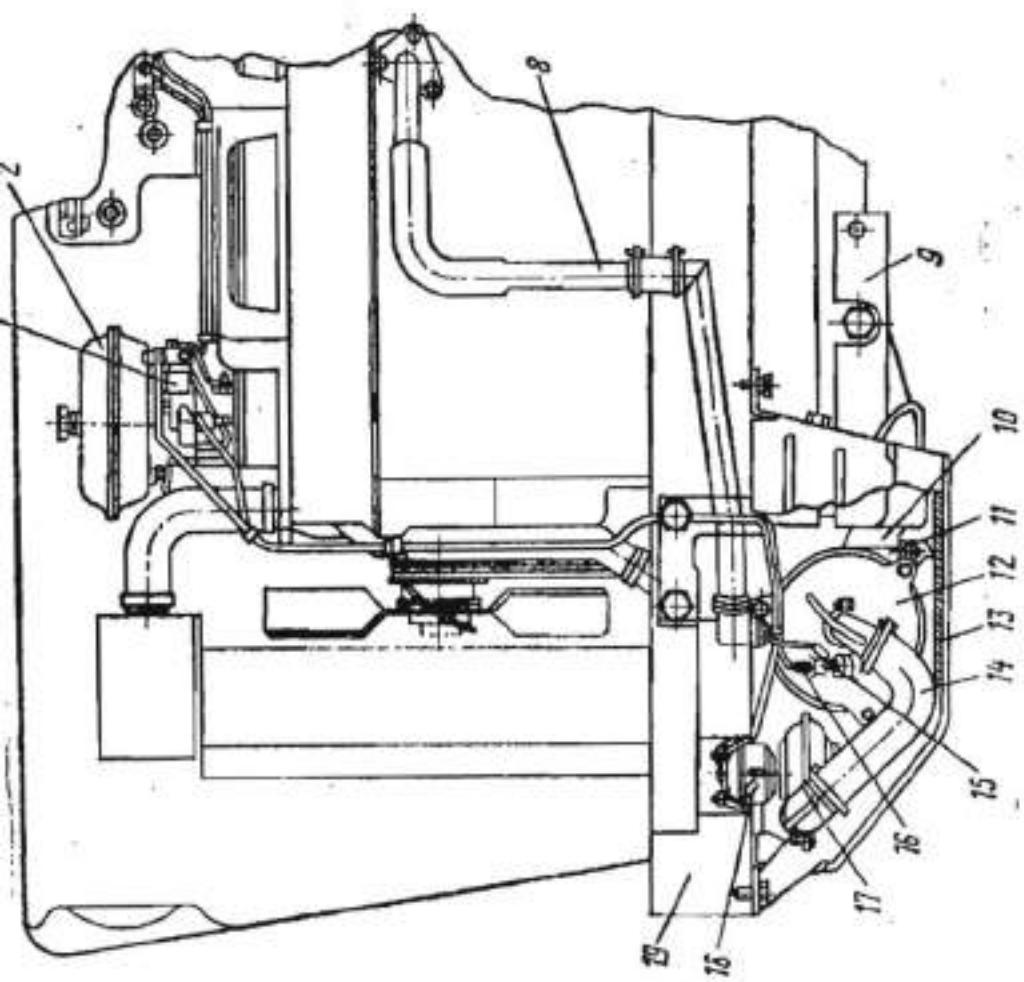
Схема установки предпускового подогревателя на двигатель:
